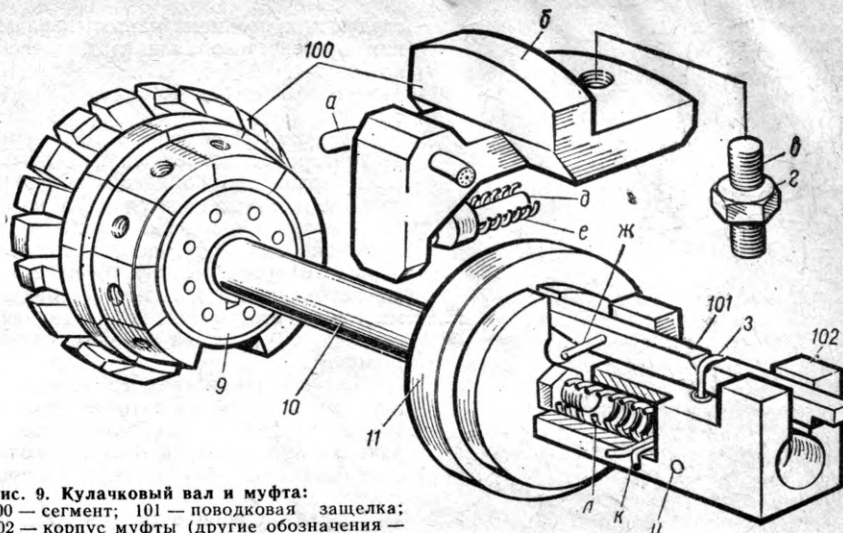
Кулачковый вал и муфта: 100 — сегмент; 101 — поводковая защелка; 102 — корпус муфты (другие обозначения — общие с рис. 1)
